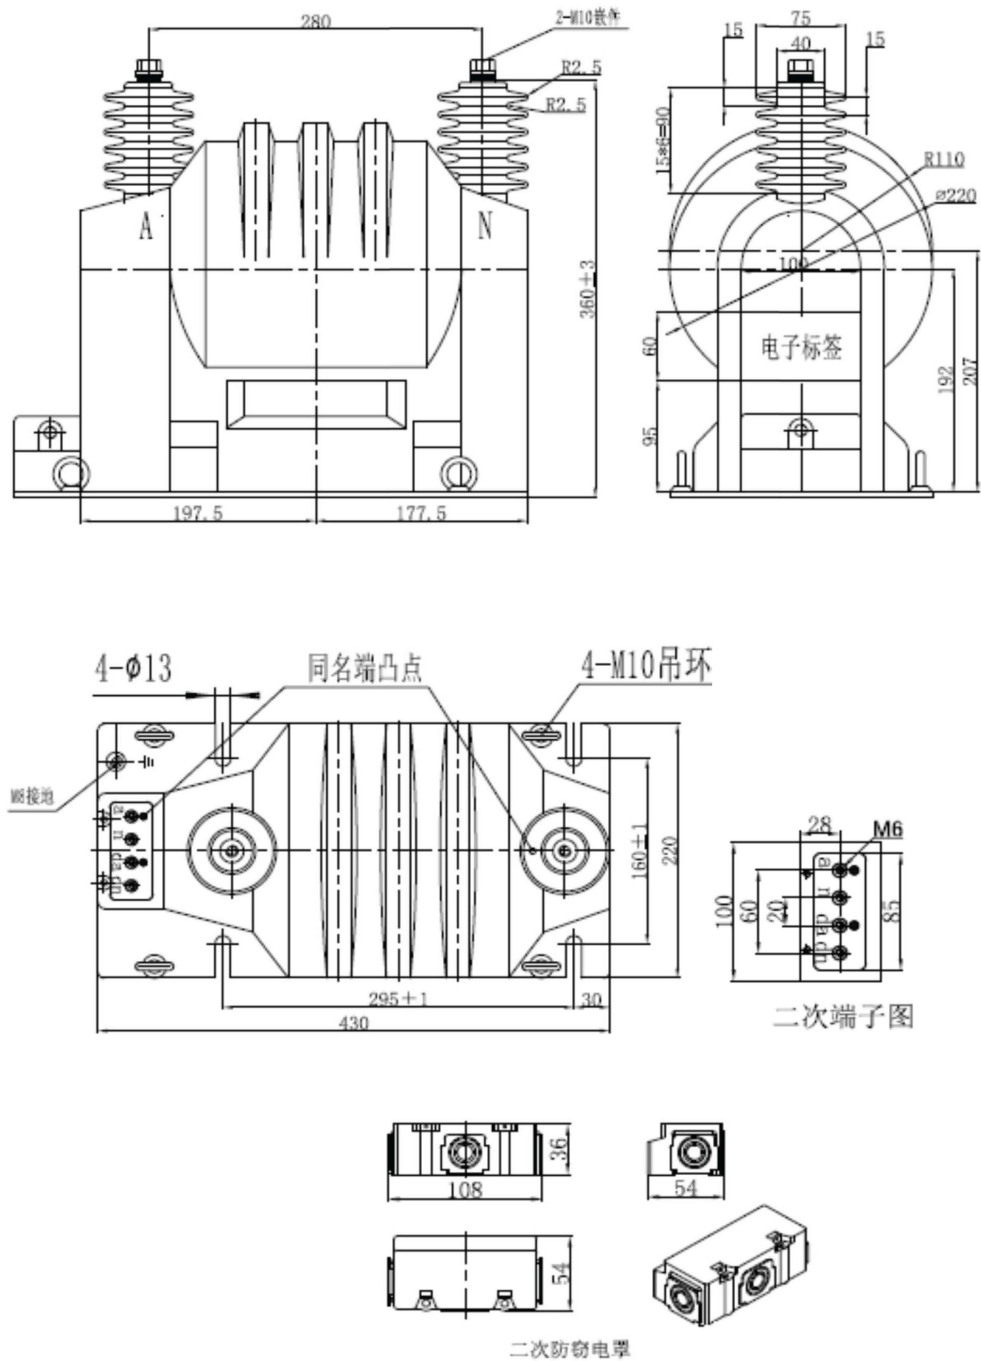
JDZYN-20型接地式电压互感器外形尺寸 (mm)
